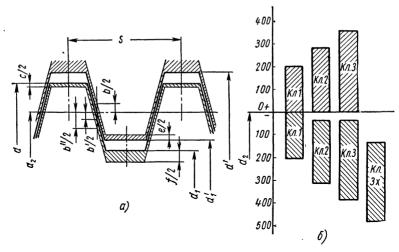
Схемы расположения полей допусков на трапецеидальную резьбу: a — общая схема; δ — допуски по среднему диаметру в $m\kappa$
